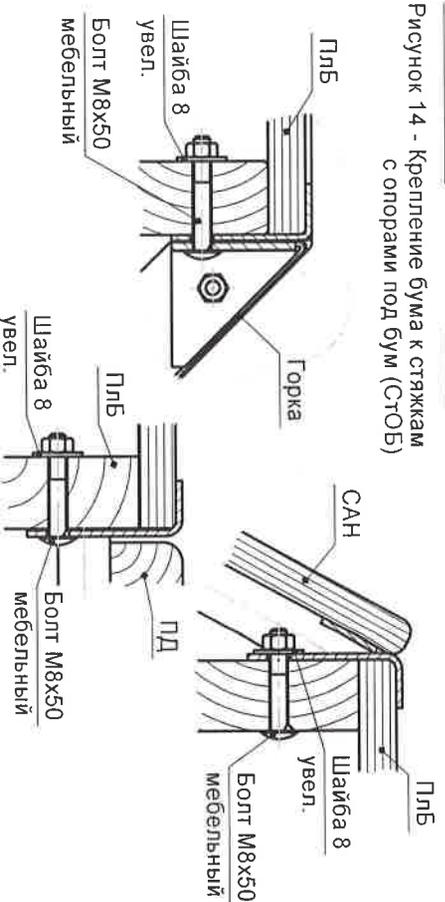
Крепление пандуса деревянного (ПД), стенки альпинистской наклонной (САН) и горки к площадкам башен (ПлБ)
